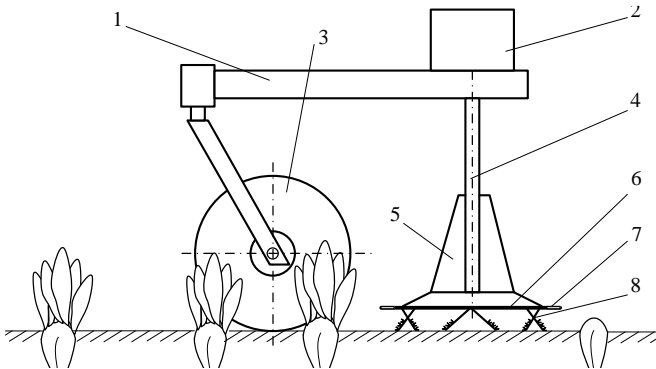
Загальний вигляд апарата для одночасного зрізування гички і очищення головок коренеплодів: 1 – рама; 2 – редуктор; 3 – опорне колесо; 4 – вертикальний вал; 5 – бітер; 6 – горизонтальний диск; 7 – ніж; 8 – копіювальний робочий елемент
